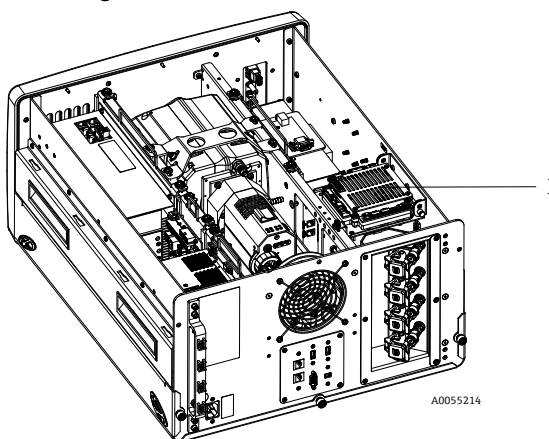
Vue d'ensemble arrière avec plaque de contrôleur en position normale (1)
